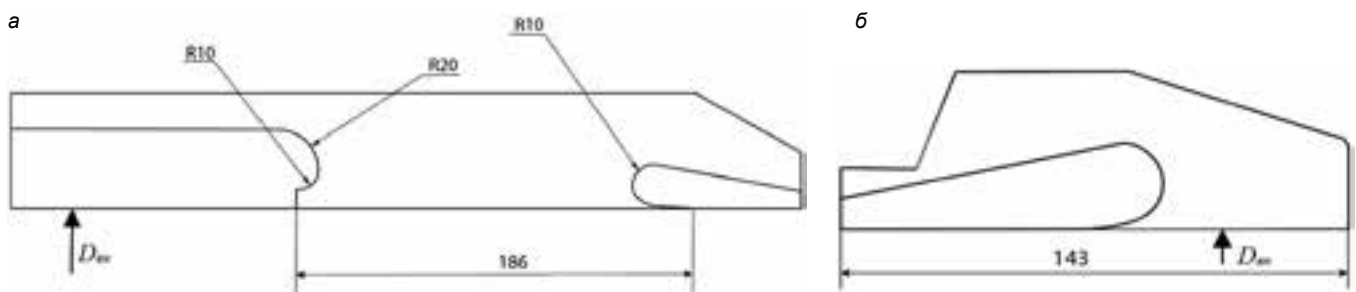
Конструкционные размеры отливки соединительной (а) и концевой (б) муфты, размеры даны в мм
